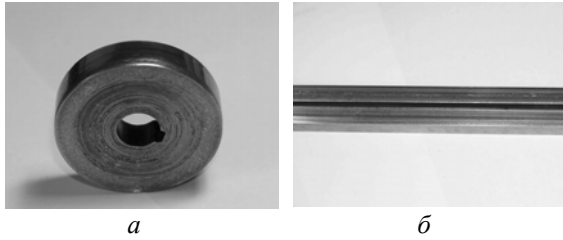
Модельні зразки колеса (а) і рейки (б)
